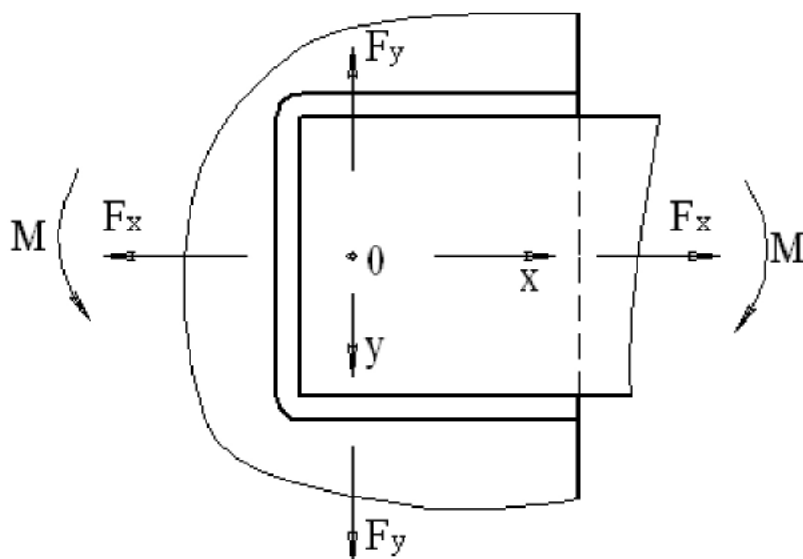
Схема сварного соединения, нагруженного силами и моментом
